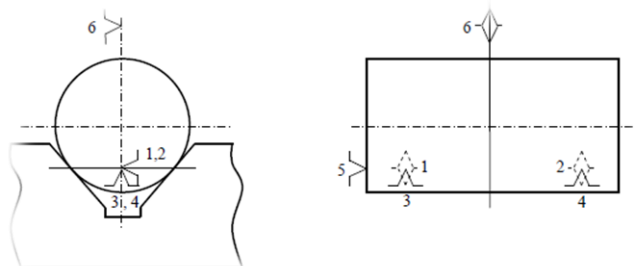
Установка цилиндрической заготовки в призмах опорных
